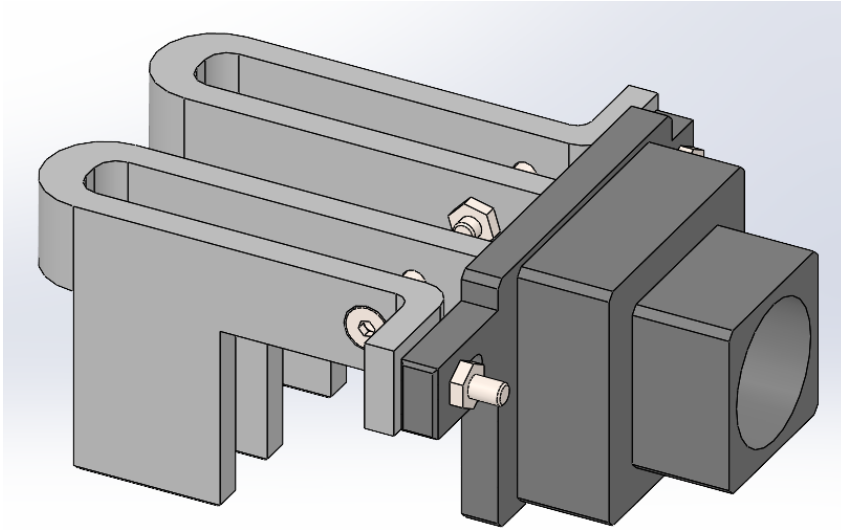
Vista isométrica 1 (Fuente: Solidworks)
